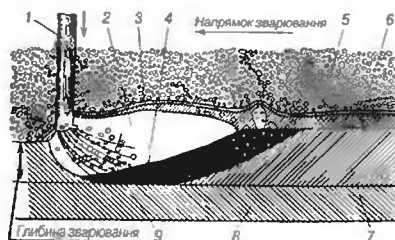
Схема горіння зварної дуги під флюсом:
